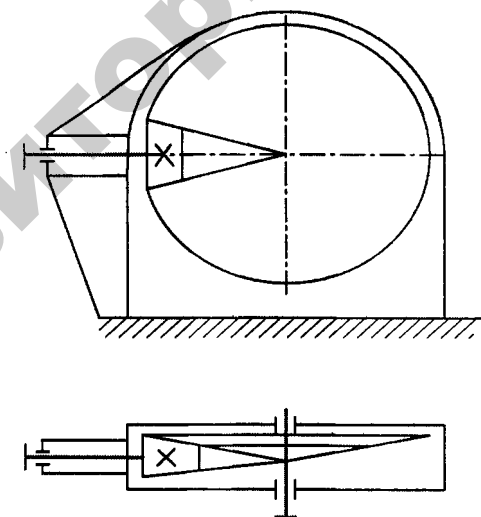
Зубчатый одноступенчатый конический редуктор
